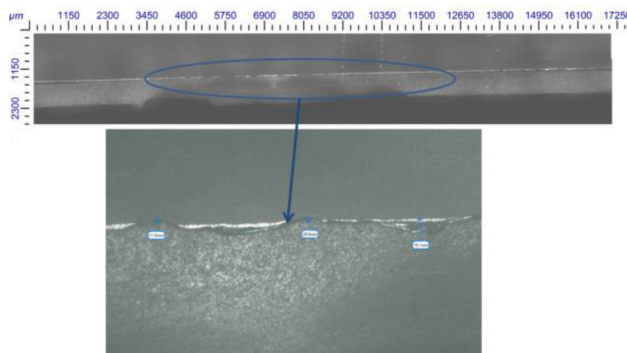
Микроструктура сварного соединения образца № 1 с непроваром по всей площади сварного соединения.
